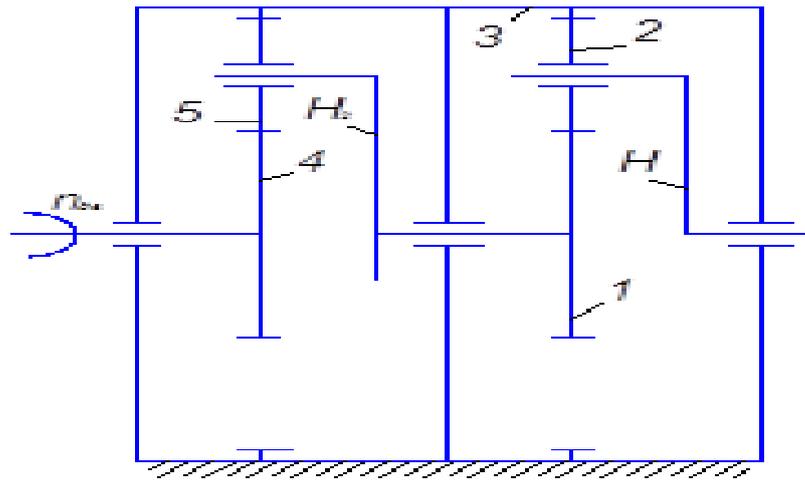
Кинематическая схема двухступенчатого планетарного редуктора
